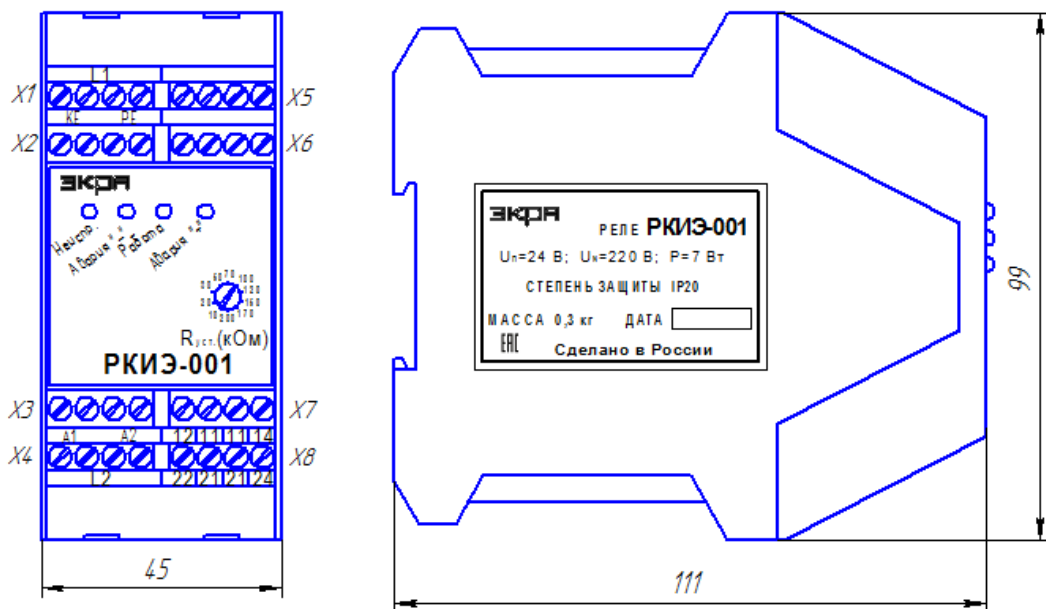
Габаритные размеры реле контроля сопротивления изоляции РКИЭ-001
